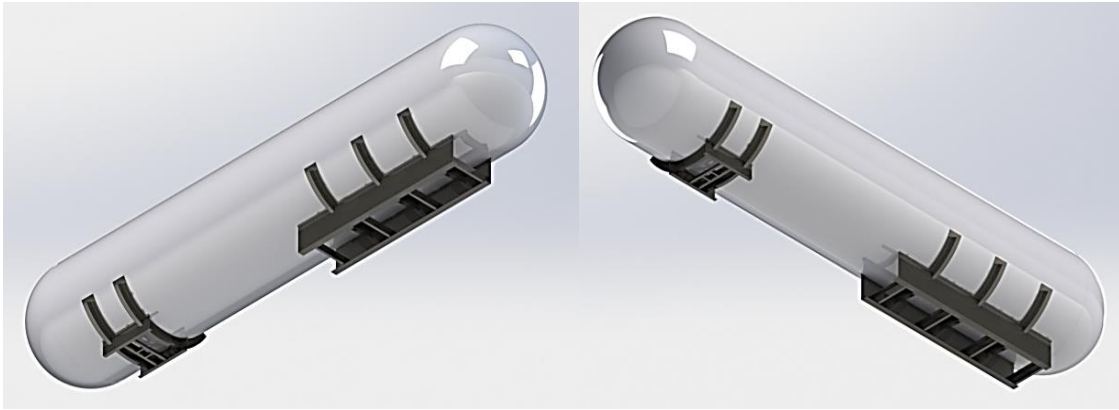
Vistas isométricas del Semirremolque tipo Tanque GLP ensamblado
